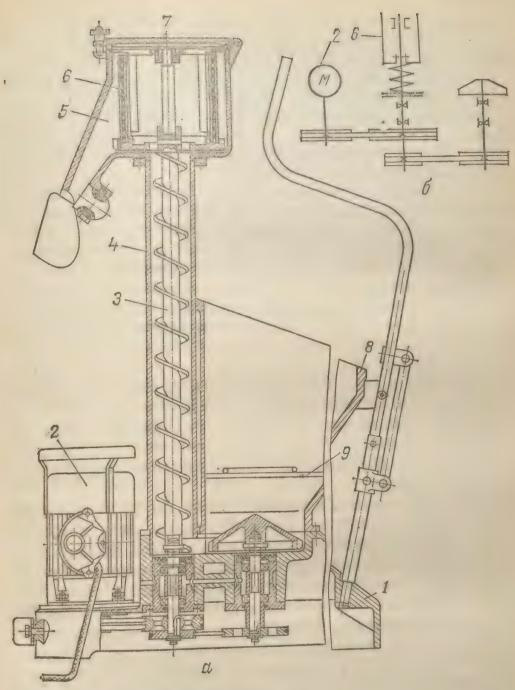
Просеиватель МПМ-800: а - общий вид; б - кинематическая схема
